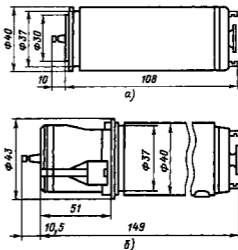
Габаритные и установочные размеры двигатель-тахогенераторов серии АДТ-40
